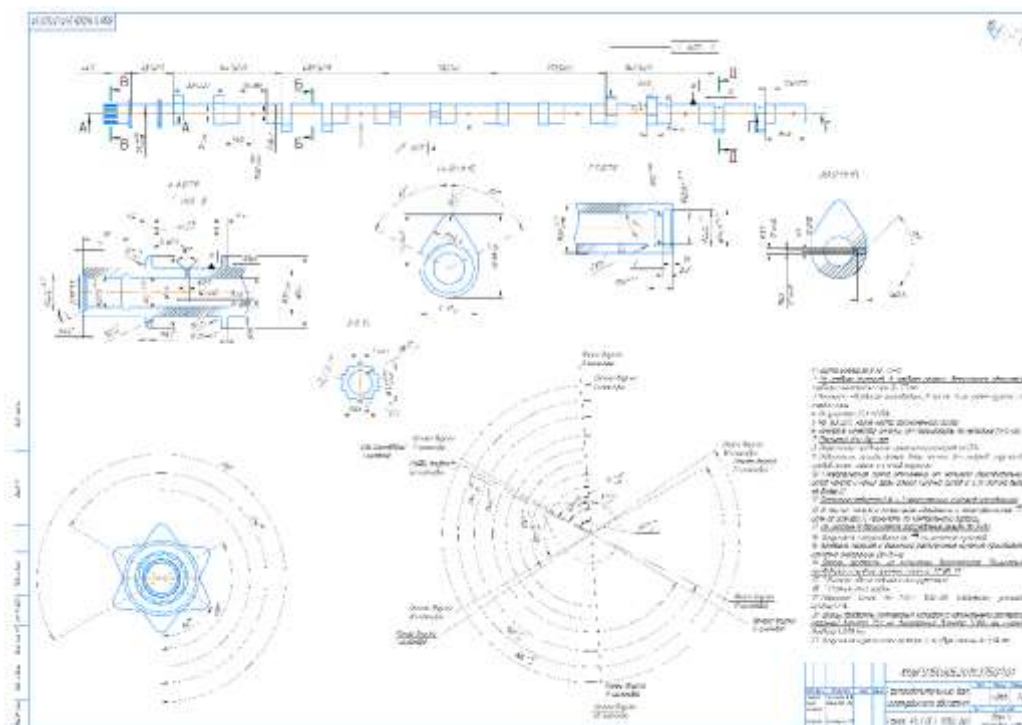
деталь «Распределительный вал газотурбинного двигателя»
